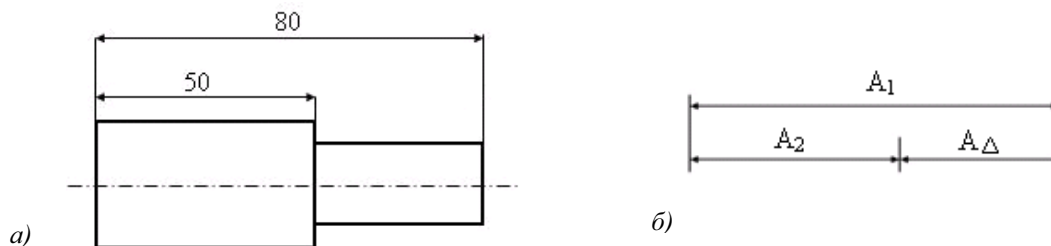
Деталь: а) эскиз, б) схема размерной цепи
